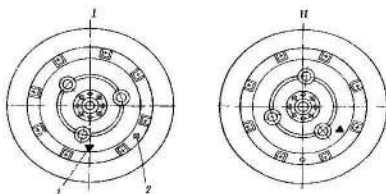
Конечная передача: 1 – треугольная метка; 2- пробки контрольного отверстия. I – положение водила для проверки уровня и заправки масла; II – положение водила для слива масла.
